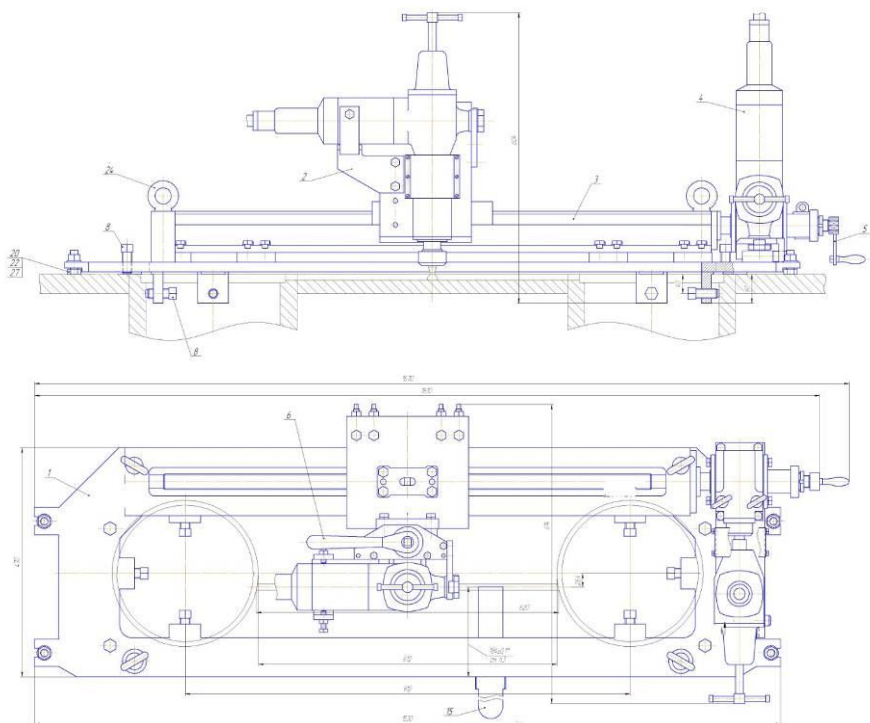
Компоновка OXZCv мобильного портативного фрезерного станка
